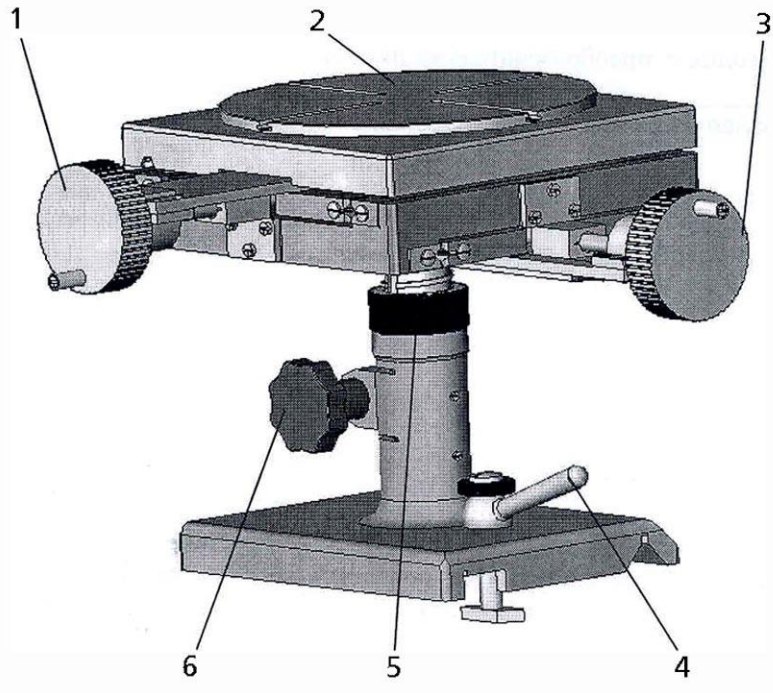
Столик двухкоординатный с преобразователями линейных перемещений
